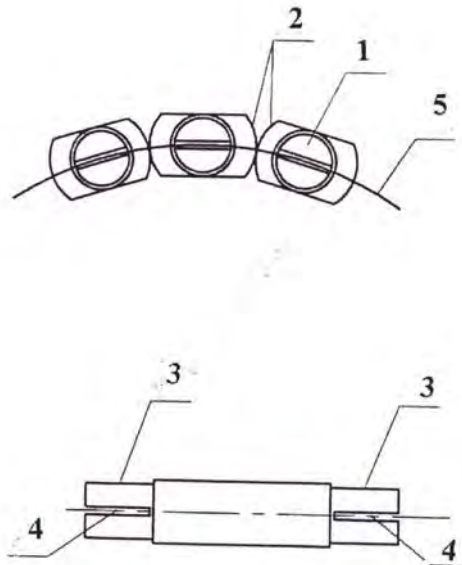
Фрагмент зубчатой цепи, работающей на сжатие
